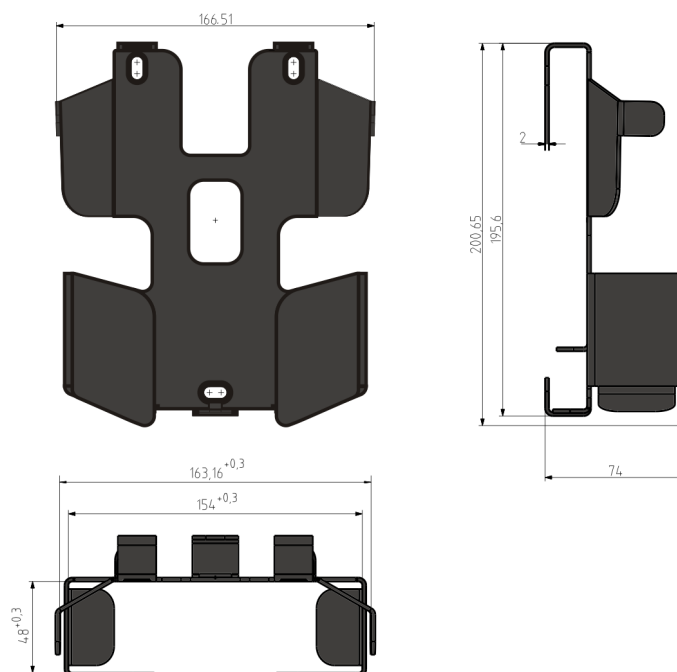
Frontansicht Wandhalterung KeTop WB020, (Maßangaben in mm)
